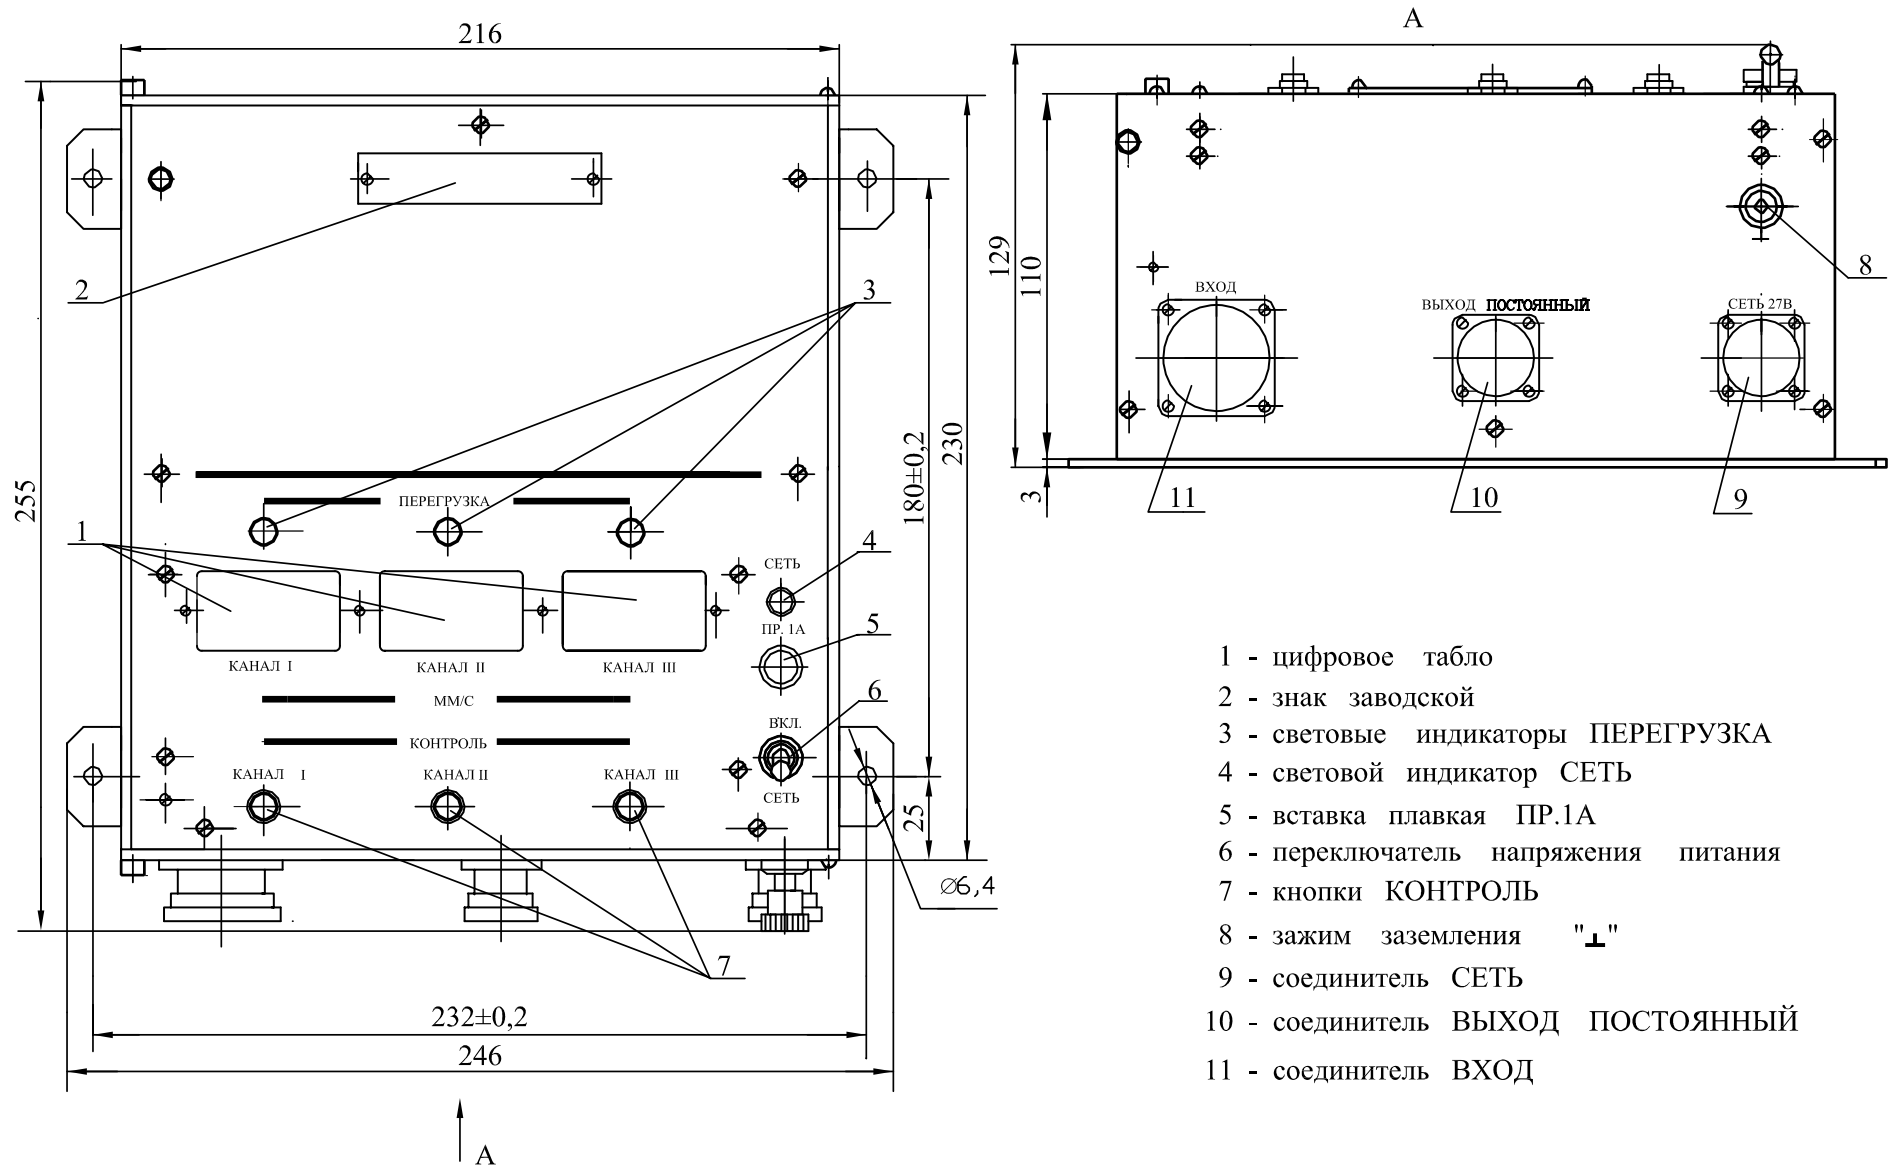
Габаритно-установочные размеры блока БЭ-39-3М.2
